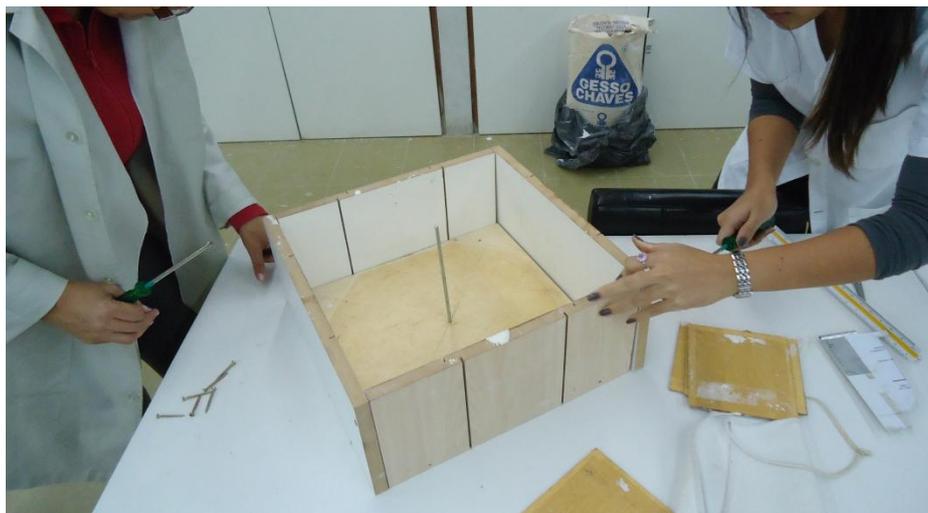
Montagem da estrutura para construção de molde na UTFPR
